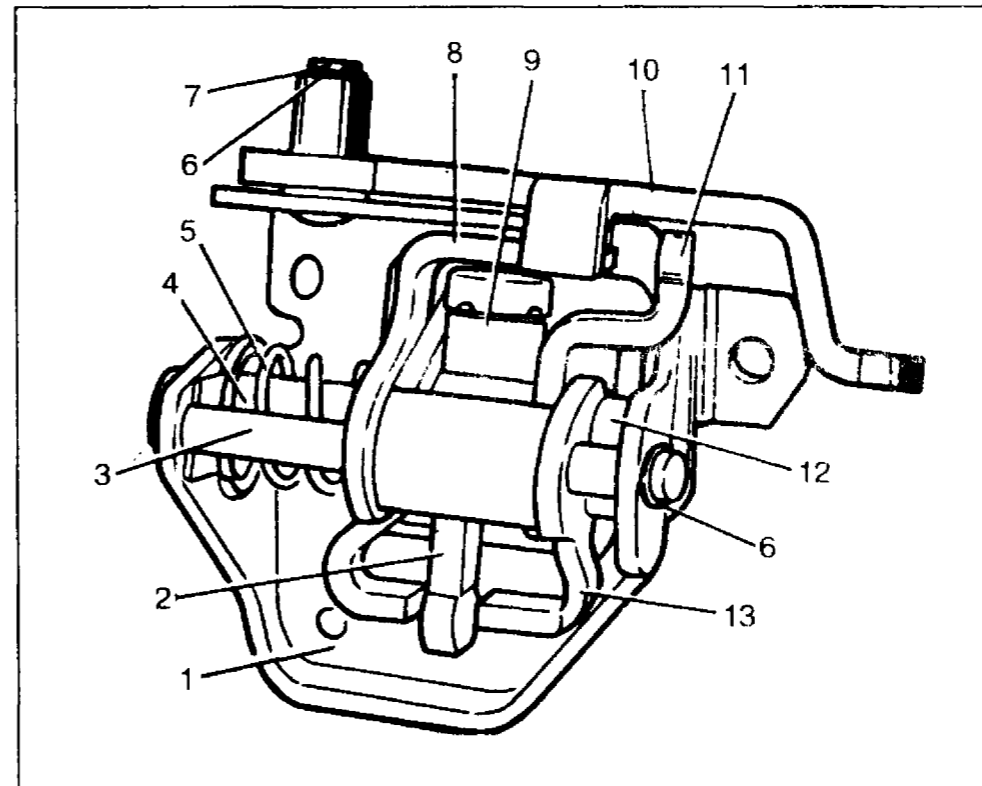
Механизм выбора передач: 1 — корпус механизма выбора передач; 2 — рычаг выбора передач (переднего хода); 3 — направляющая ось блокировочных скоб; 4 — ось рычага выбора передач; 5 — пружина; 6 — стопорное кольцо; 7 — ось вилки заднего хода; 8, 13 — блокировочные скобы; 9 — фиксатор рычага выбора передач; 10 — вилка включения заднего хода; 11 — рычаг выбора передач (заднего хода); 12 — упорная втулка
